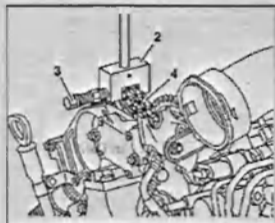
Установите приспособление 2 для рассоединения цепи на цепь 4.
